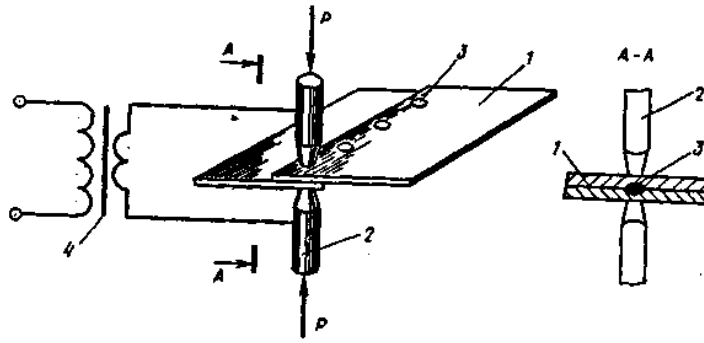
Контактная точечная сварка 1 – свариваемые детали; 2 – электроды точечной сварочной машины; 3 – сварная точка; 4 – трансформатор
